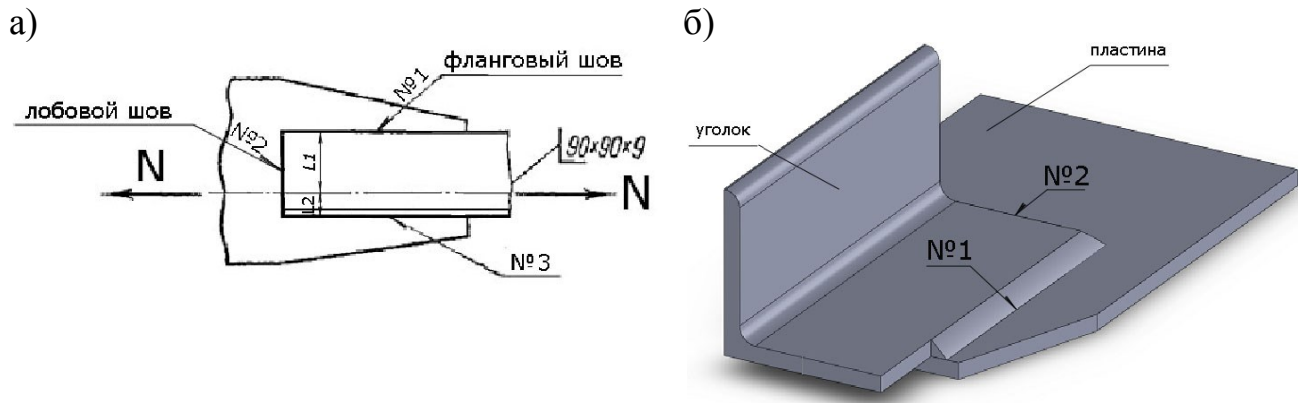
Расчет сварного соединения: а – схема нагружения; б – 3D-модель
